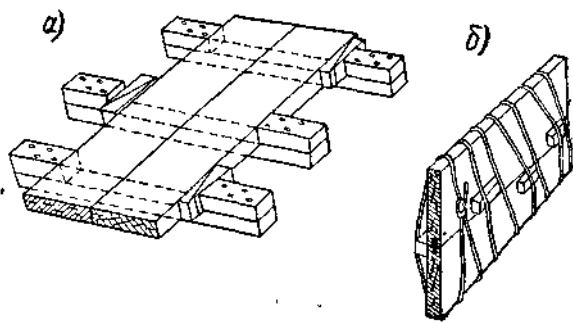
Склеивание заготовки для шверта и руля: а — запрессовка в приспособлении; б — шнуром с помощью клиньев.
